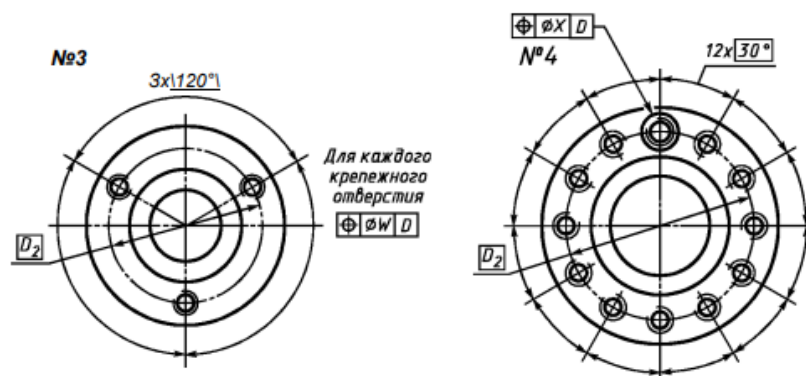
Присоединительные поверхности шпинделя А2-6
